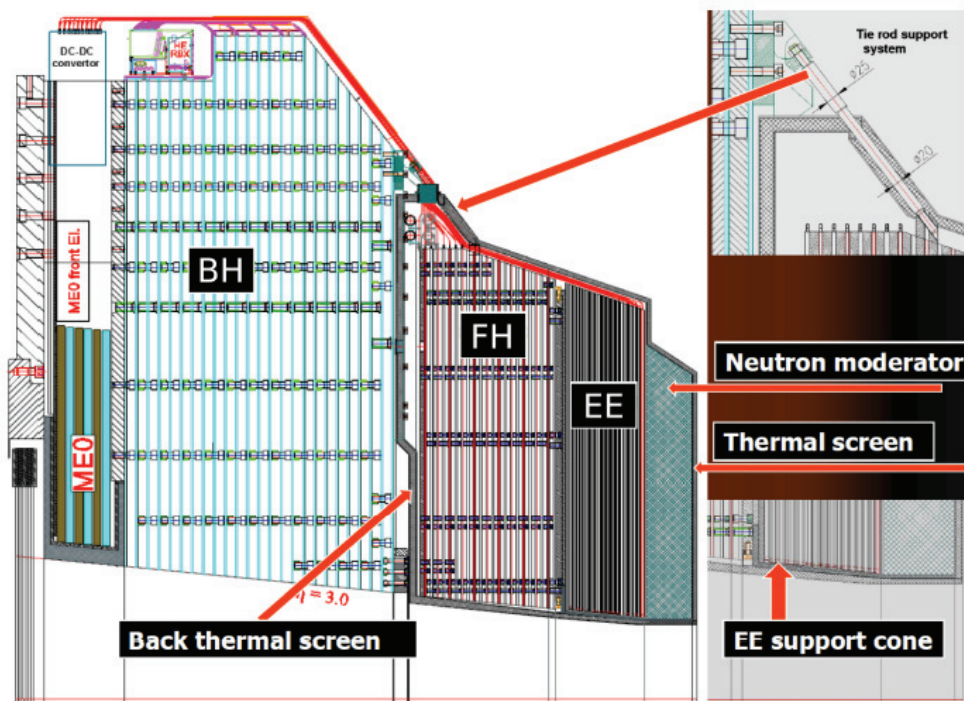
Dessin technique de la structure du HGCal [61]
